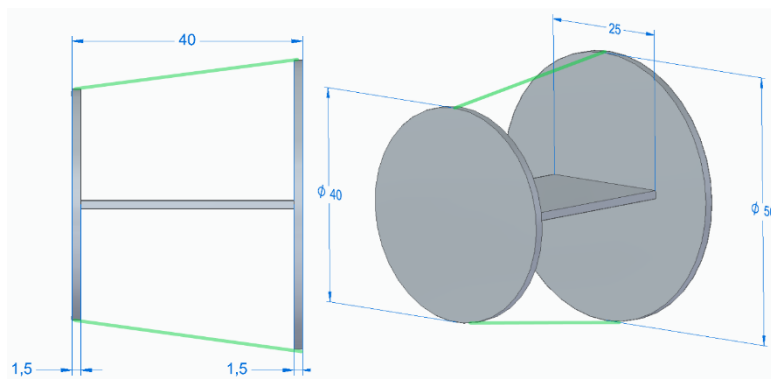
Příklad odřezku (Zdroj vlastní)
